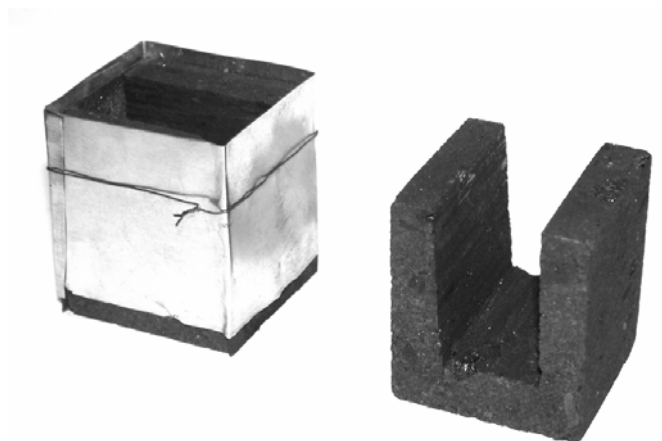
Внешний вид заготовок для изготовления образцов покрытия.
